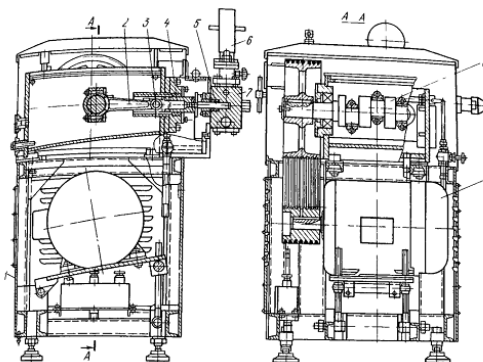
Конструкція гомогенізатора К5 – ОГА – 1,2 (1 – станина; 2 – кривошипно-шатунний механізм; 3 – палець; 4 – повзун; 5 – плунжер; 6 – манометрична головка; 7 – блок плунжерний; 8 – колінчастий вал; 9 – електродвигун.)
